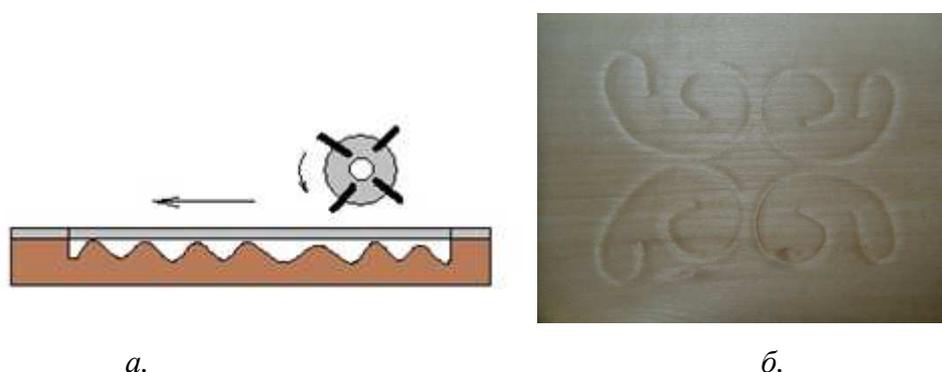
Калибрование по толщине: а. фрезерование; б. рисунок с мнимым оттиском на поверхности детали из древесины липы после фрезерования
